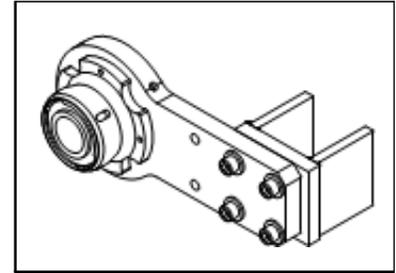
MONTAJE RODAMIENTO ESFÉRICO DE UN ÚNICO BRAZO
